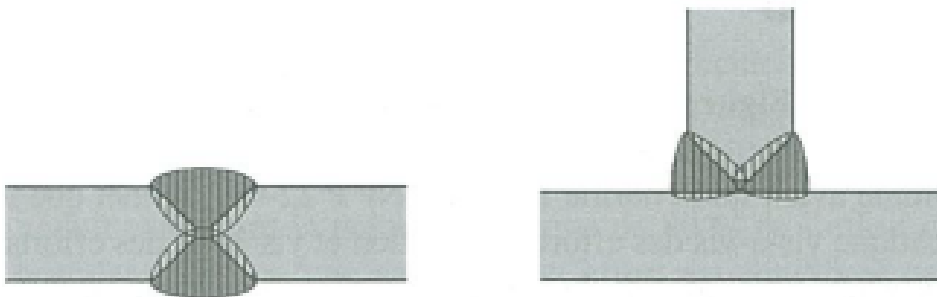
Joint de soudure à double pénétration
